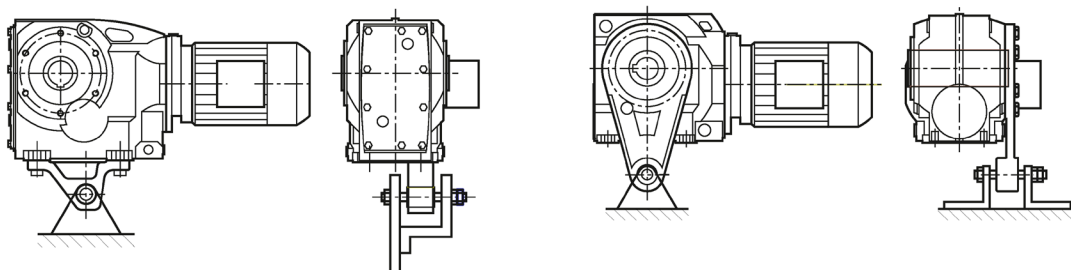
Montagevorschlag für Drehmomentstütze am Fuß und Flansch
